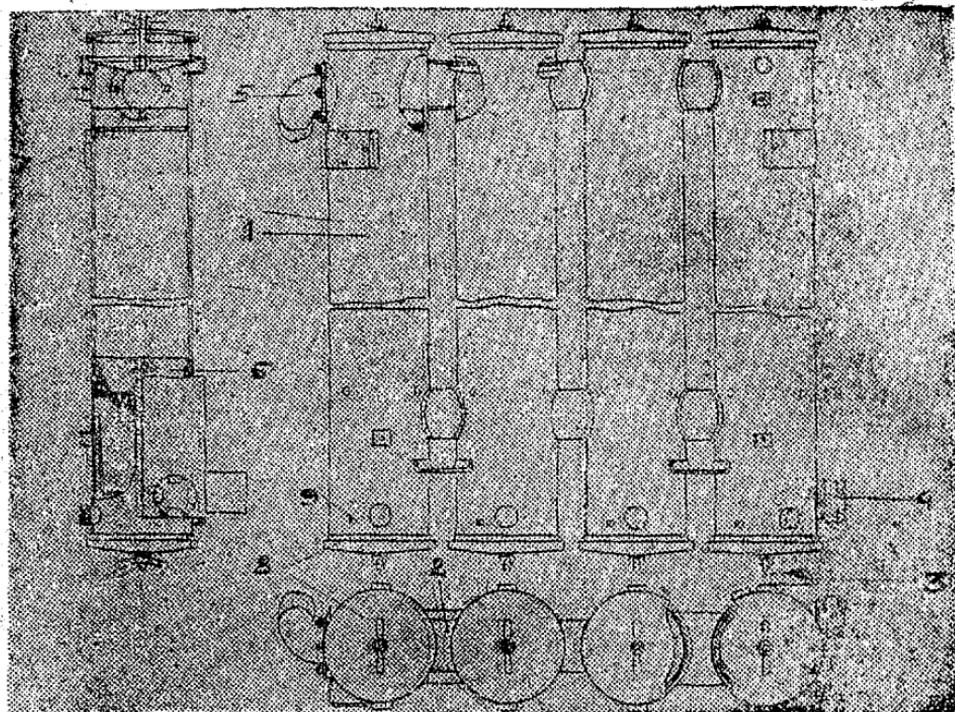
Фильтр в сборе: 1—корпус цилиндра; 2—соединительные патрубки; 3—патрубок подвода газа; 4—пробка; 5—патрубок вывода газа; 6—коническая решетка опоры; 7—кольца Рашига; 8—крышки фильтра; 9—сливные трубки.
